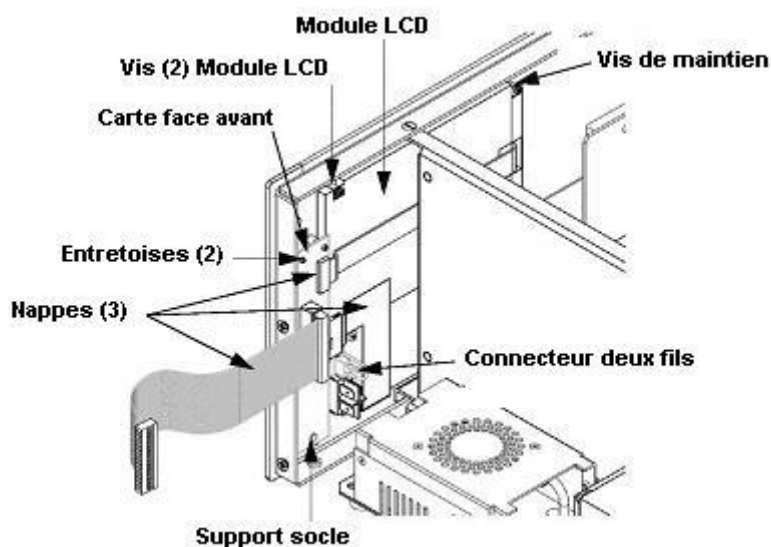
Remplacement de la carte face avant et du module LCD
